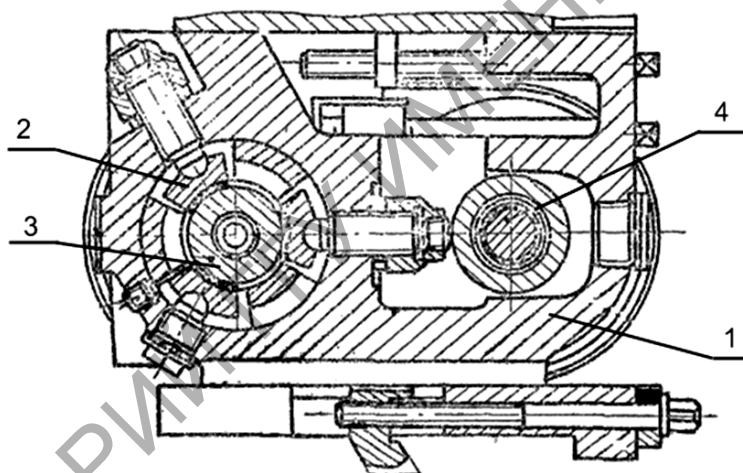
Бабка изделия шлифовального станка (модель 3У10А)
